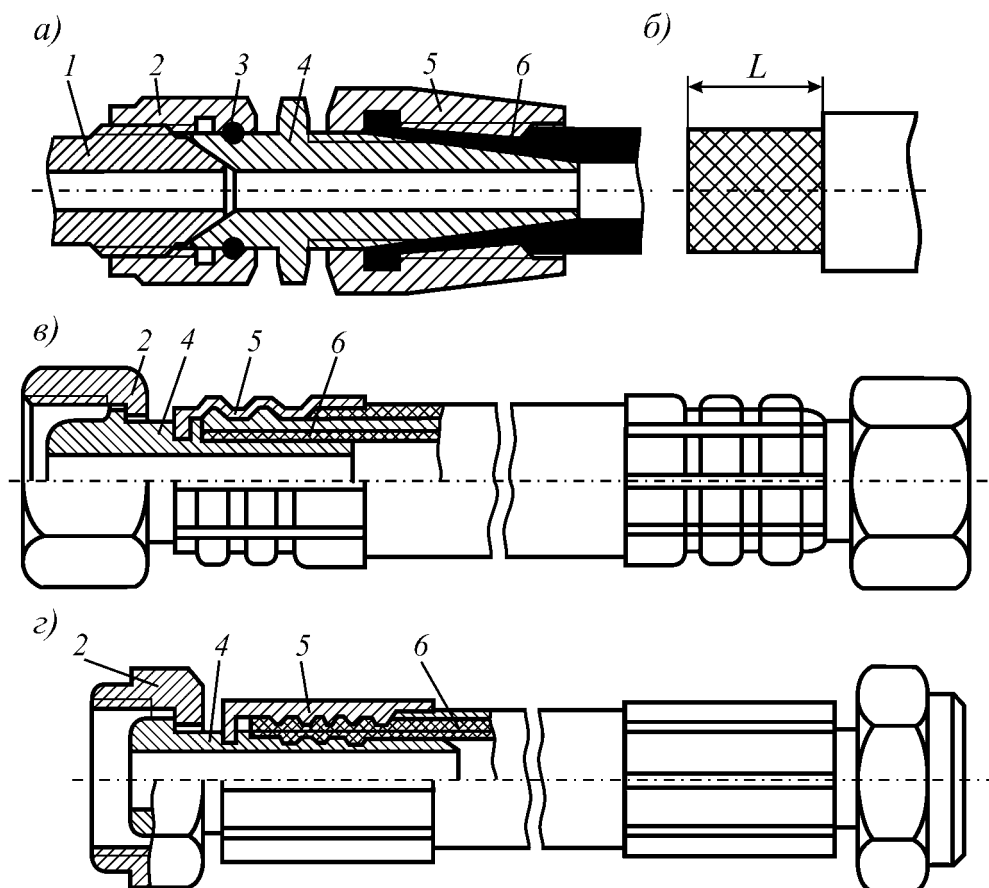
Устройство рукавов высокого давления (шлангов): *а)* с разъемным накопником (фитингом); *б)* срезка верхнего слоя резины на длину L перед монтажом; *в)* навивочной конструкции; *г)* навивочной конструкции по ТУ 22-4756-80: 1 – штуцер на сопрягаемой части машины; 2 – накидная гайка; 3 – стальное кольцо; 4 – ниппель; 5 – муфта; 6 – многослойный резиновый рукав с металлическими оплетками
